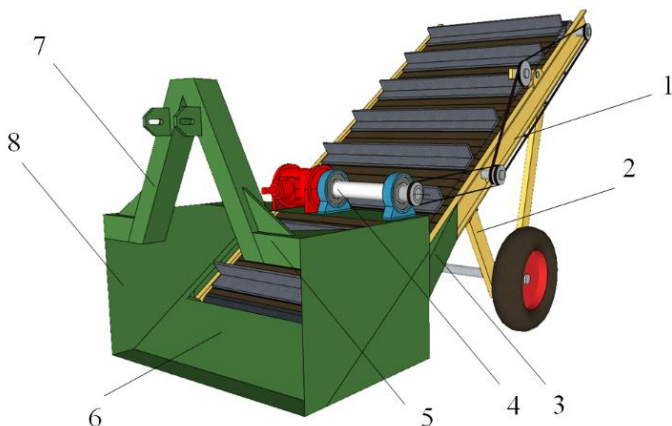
Машина для удаления и погрузки тепличного грунта: 1 – отгрузочный транспортер; 2 – рама; 3 – соединительные полосы; 4 – механизм привода; 5 – верхняя часть; 6 – ковш; 7 – система агрегатирования; 8 – отвал
